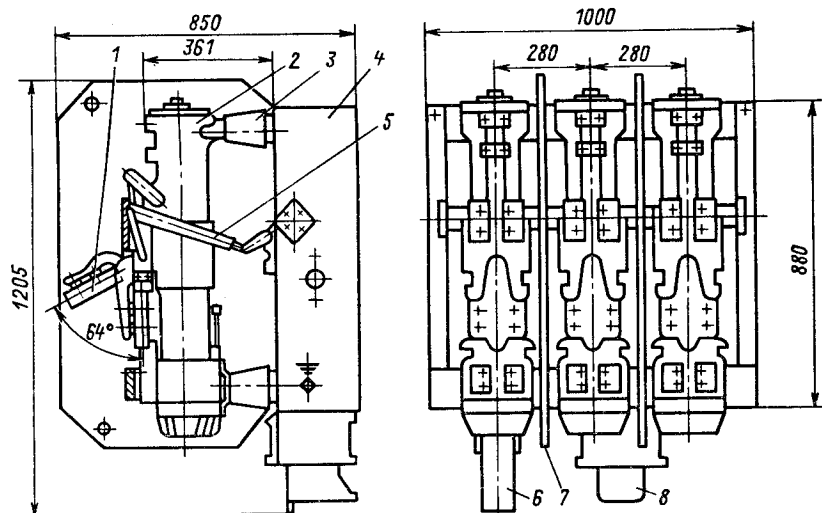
Общий вид выключателя ВМПЭ-10 на номинальные токи 2500 и 3150 А: 1 — рабочий подвижный контакт; 2 — корпус выключателя; 3 — изолятор; 4 — стальная рама, 5 — изоляционная тяга; 6 — контактор; 7 — изоляционная перегородка; 8 — привод
